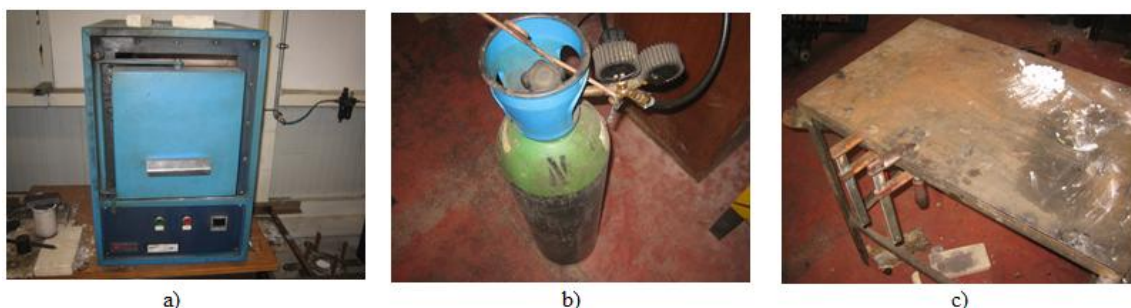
Componentes usados nos ensaios de soldadura: a) mufla; b) Garrafa de árgon; c) mesa de soldadura.
